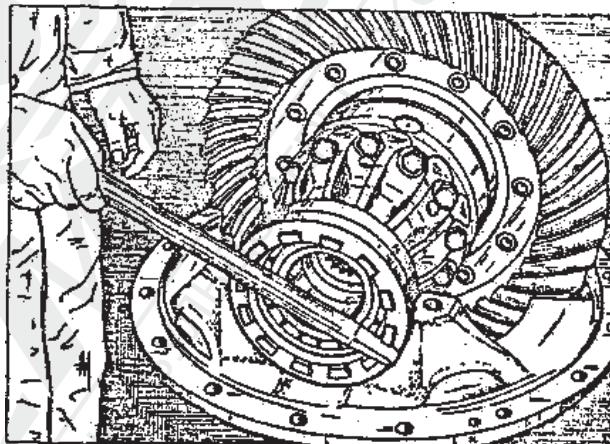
Регулировка положения узла тарельчатого колеса с дифференциальным механизмом относительно приводного валика.
